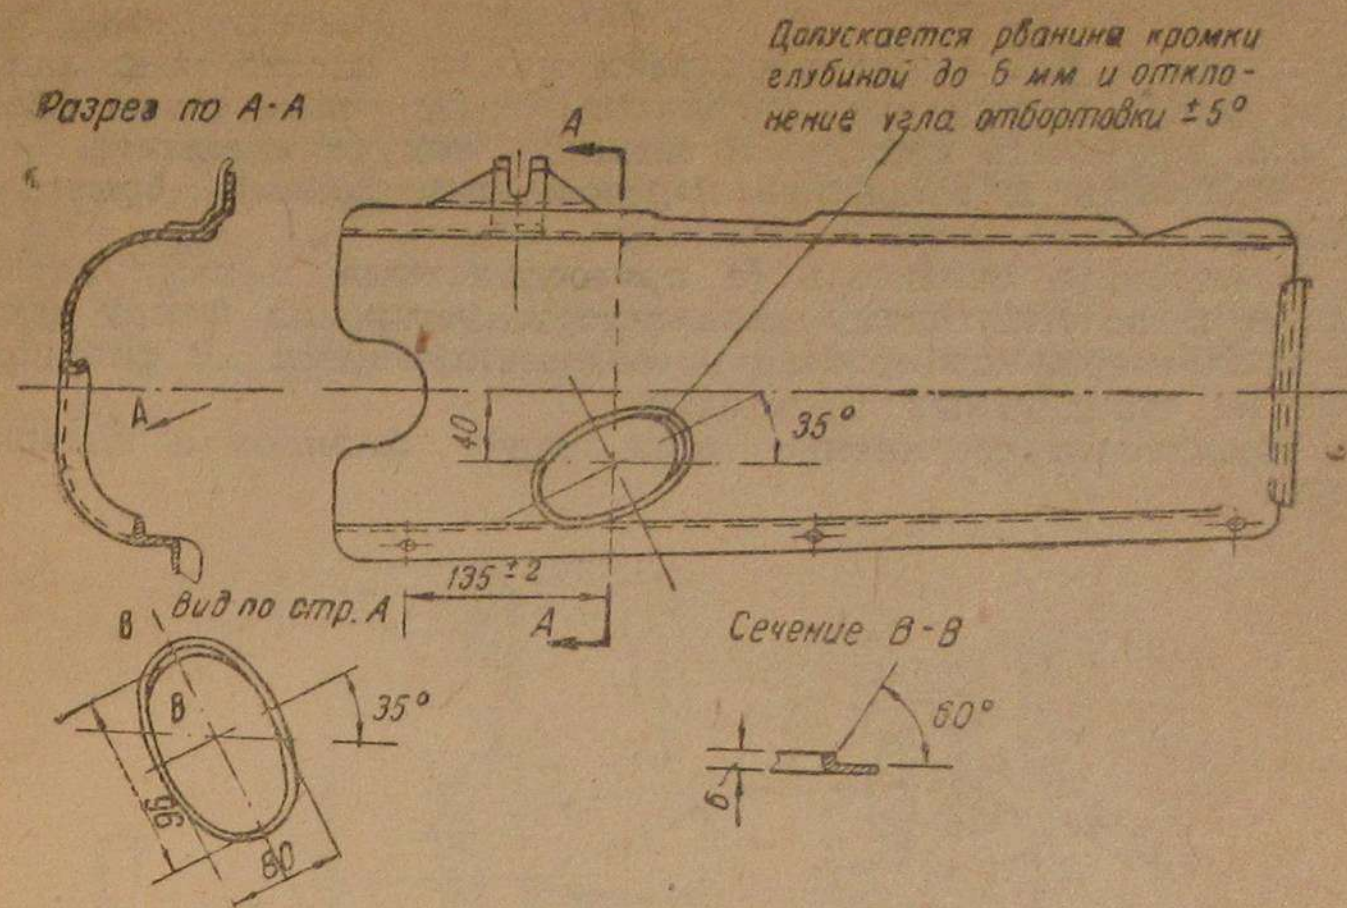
Правый брызговик двигателя ГАЗ-АА в измененном виде.
